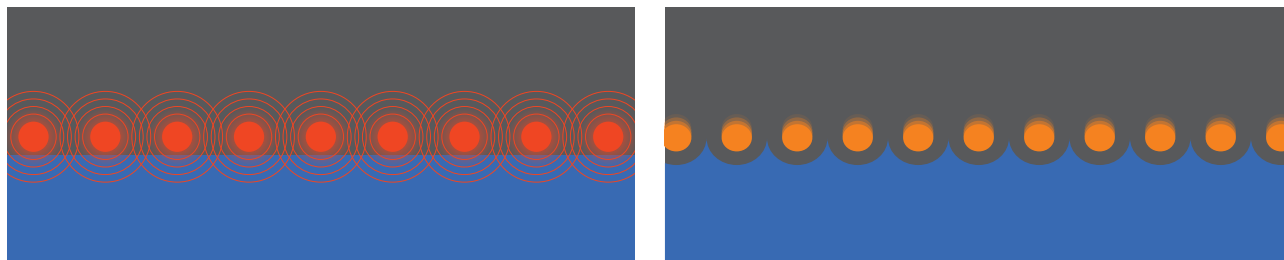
Сварка с открытой катушкой и конечная «сварочная волна»
